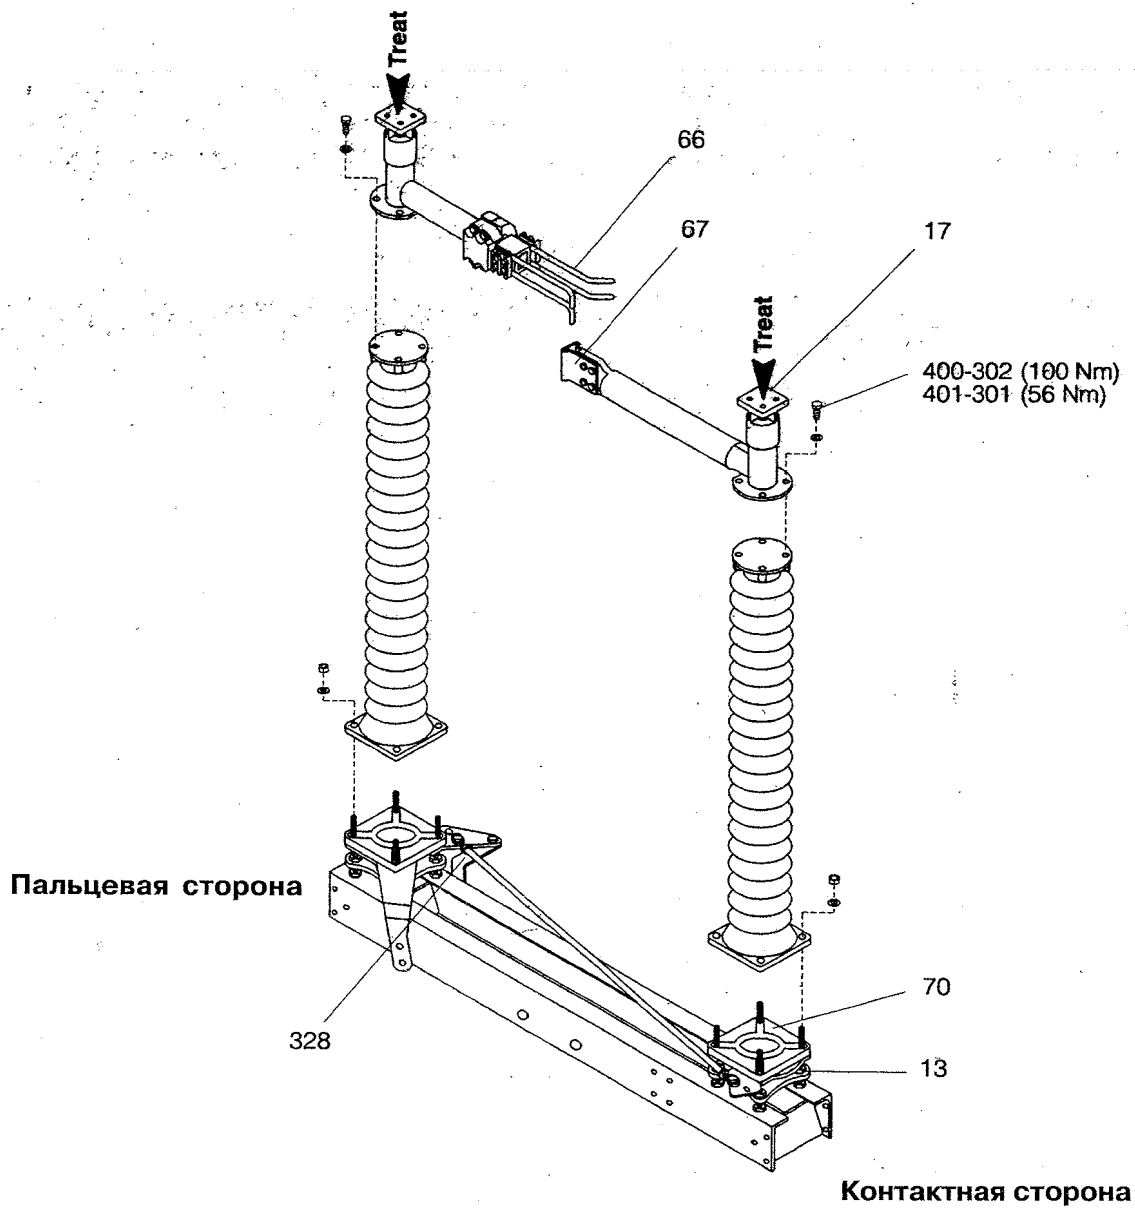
Установка тяг разъединителя; раздельная установка. Общий вид
